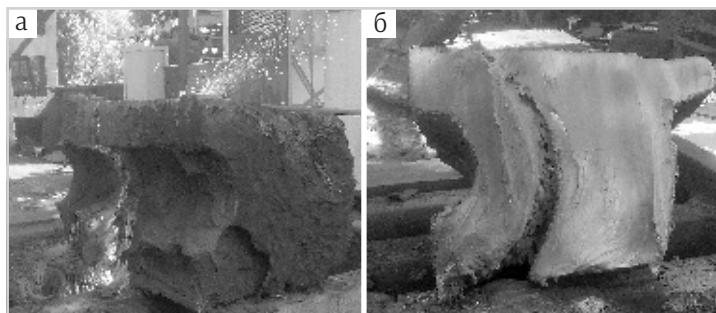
Кислородная резка заготовки сложной формы толщиной 1200 мм: а — с большим расслоением по линии реза; б — поверхность реза заготовки
